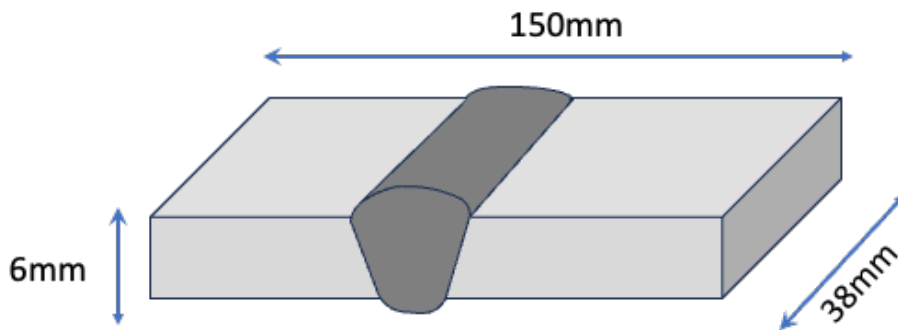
Dimensional do corpo de prova de dobramento.
